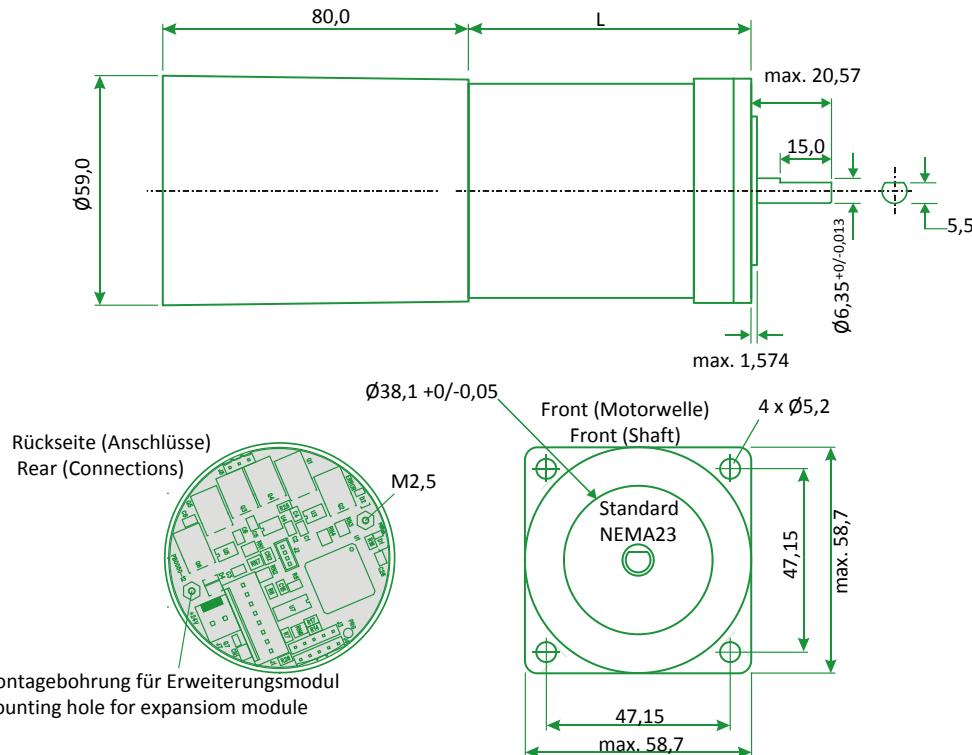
MAC050 - MAC141 Zeichnung ohne Erweiterungsmodul, Dimensionen [mm]
